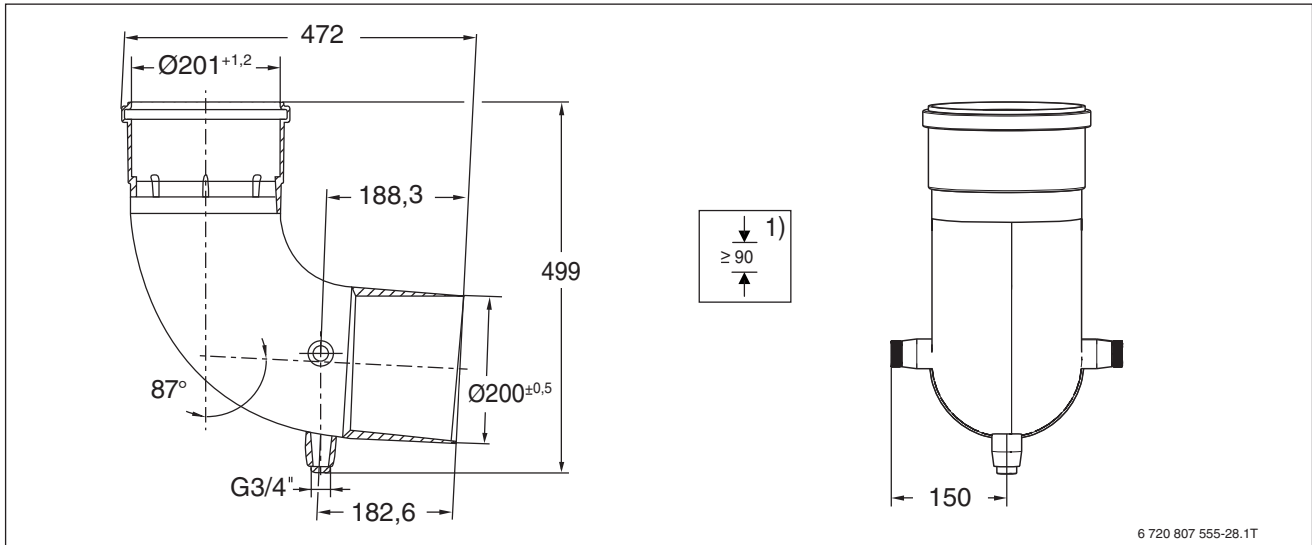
Anschlusswinkel 87° DN 200 (Maße in mm)
